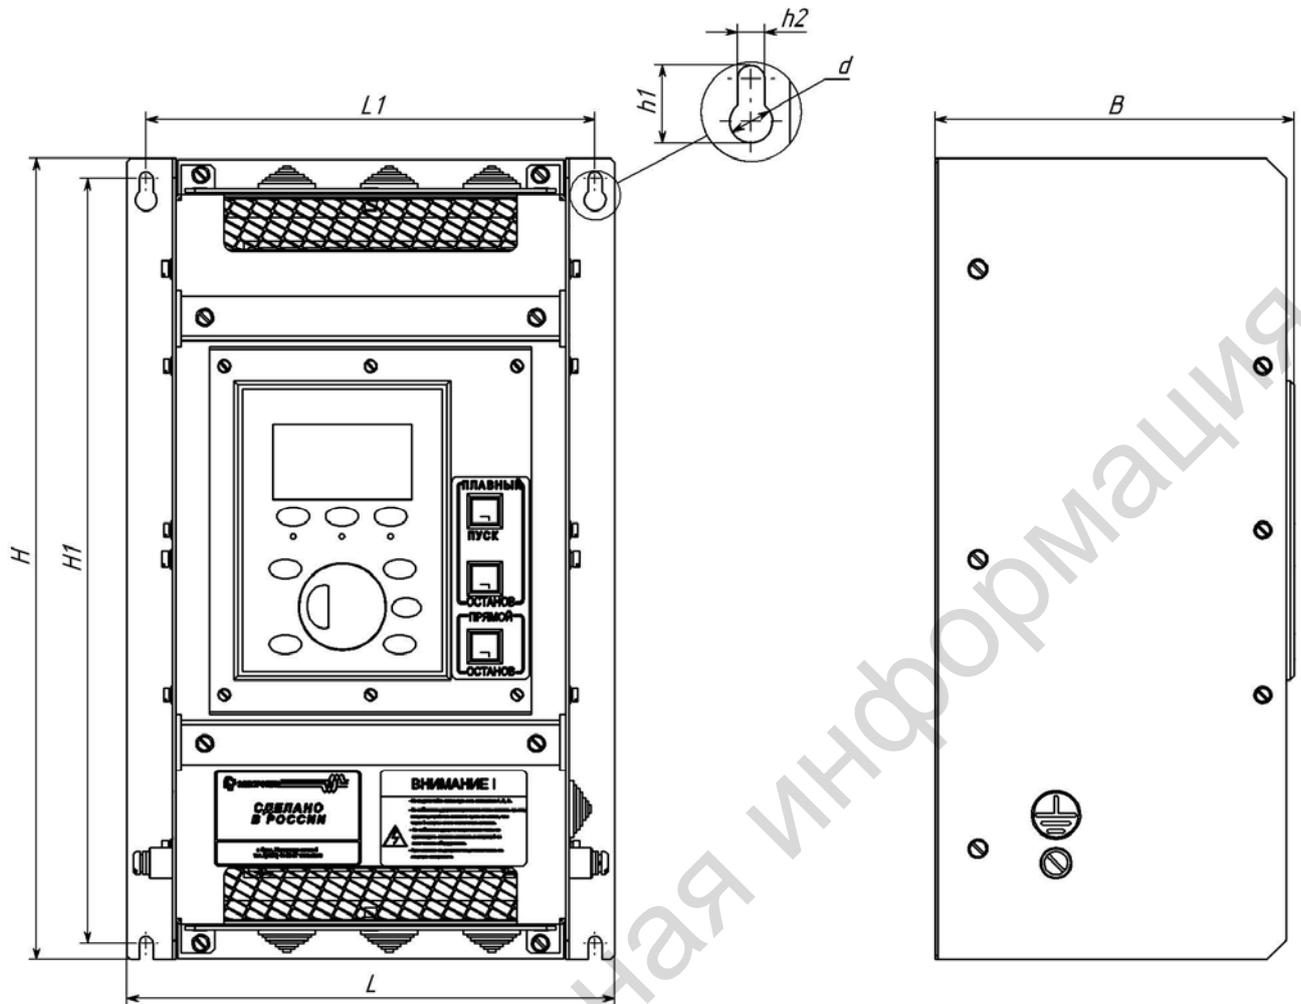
а - Габаритные и установочные размеры УПП 18,5-37
